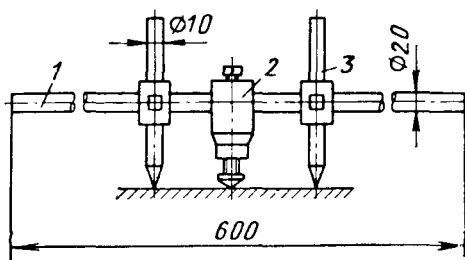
Приспособление для вырезки прокладок: 1 — стержень-рукоятка; 2 — центрирующий упор; 3 — нож
